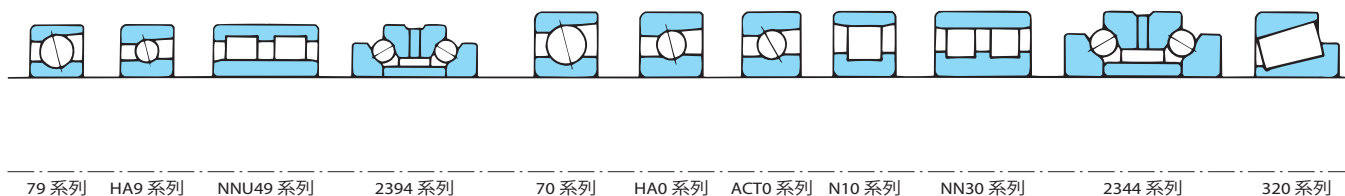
机床用精密滚动轴承的形式和各尺寸系列的轴承安装空间
